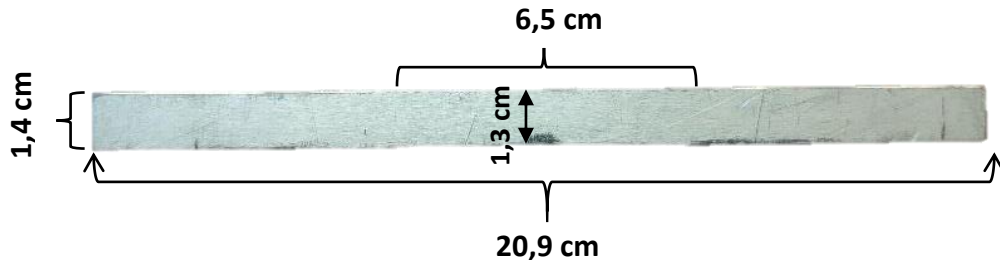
Dimensiones de la probeta AcNb. Espesor de 4 mm.
